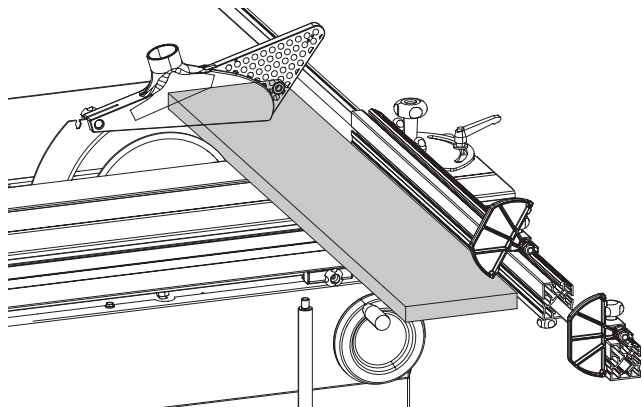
Cortes longitudinales con la regla de carro
